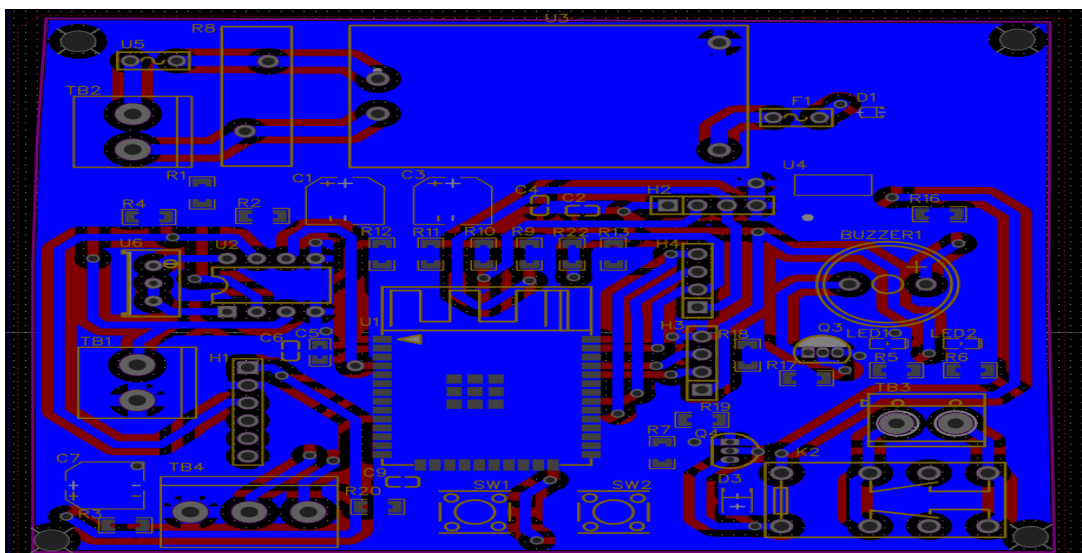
Diseño Pcb capa inferior. Fuente: (Elaboración propia)
